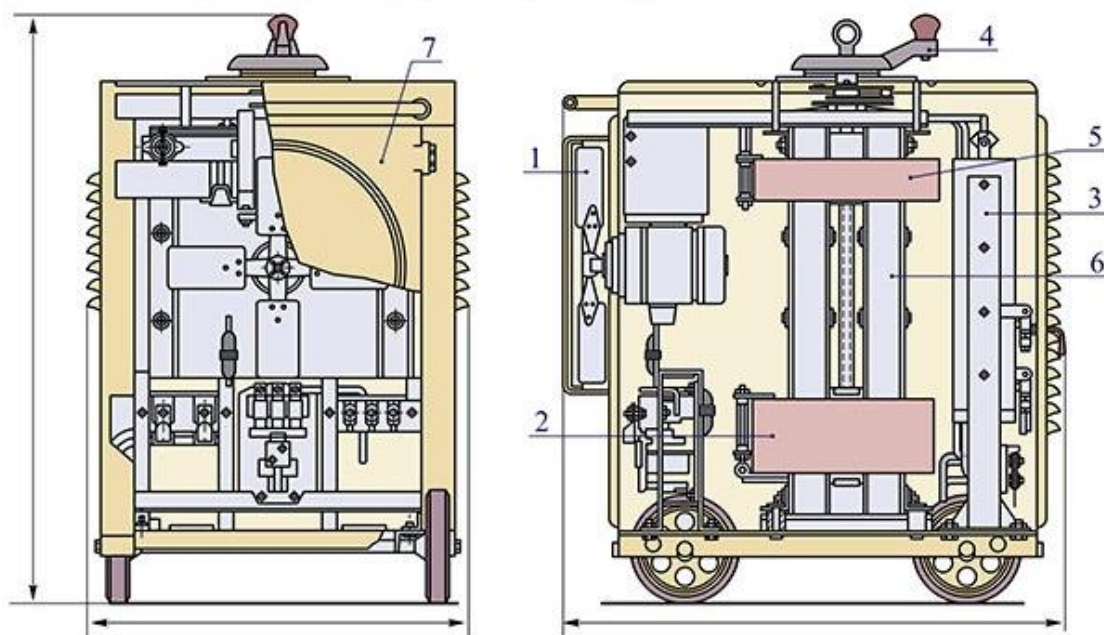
Конструктивное исполнение сварочного выпрямителя: 1 – вентилятор; 2 – неподвижная обмотка; 3 – магнитопровод трансформатора; 4 – рукоятка с механизмом перемещения подвижной обмотки трансформатора; 5 – подвижная обмотка трансформатора; 6 – блок выпрямителей; 7 – кожух
